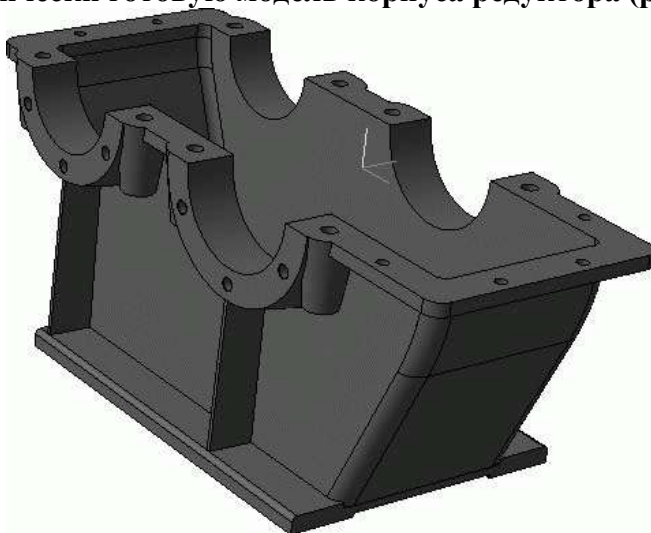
Вырезание отверстий под болты в бобышках и под подшипники в корпусе
